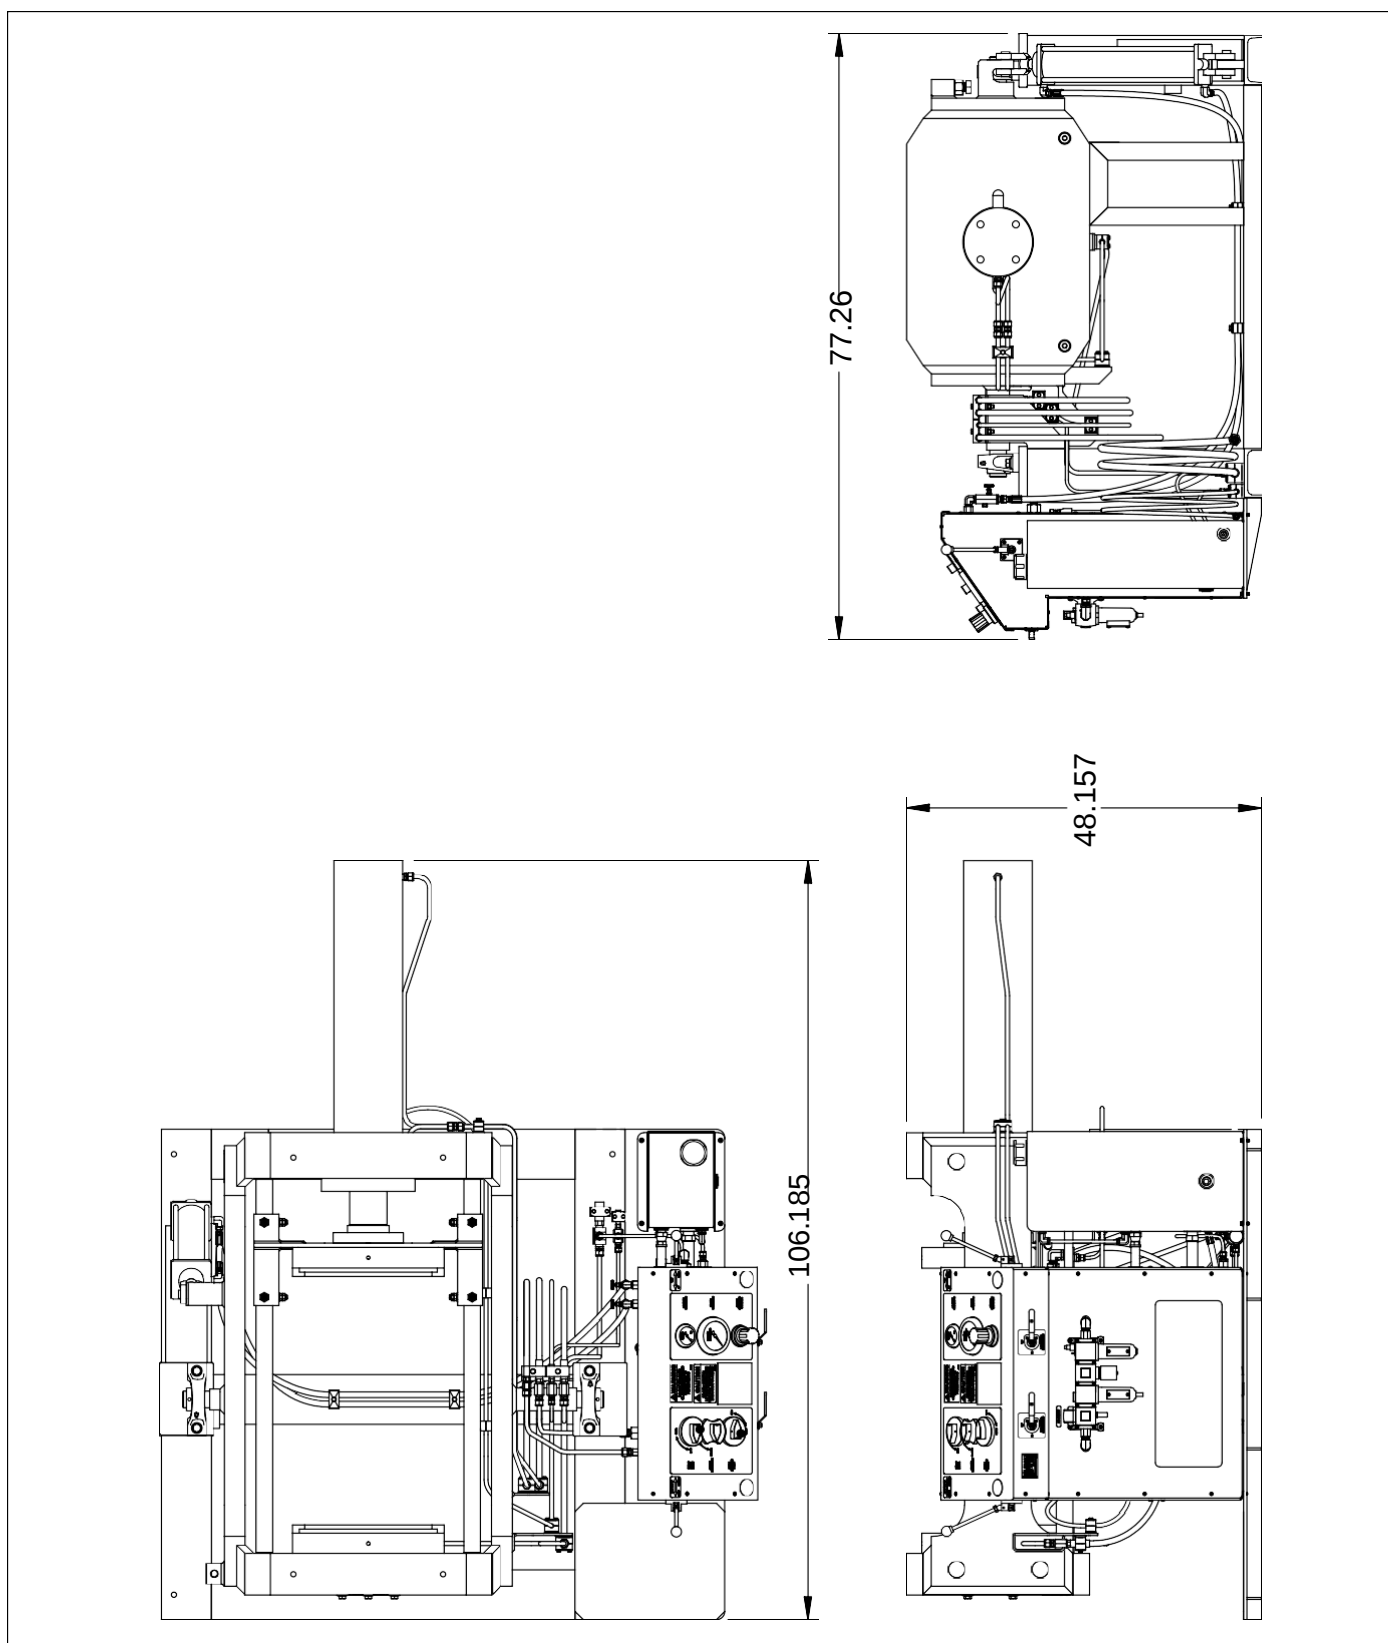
DIMENSIONS DU SYSTÈME DE SERRAGE
